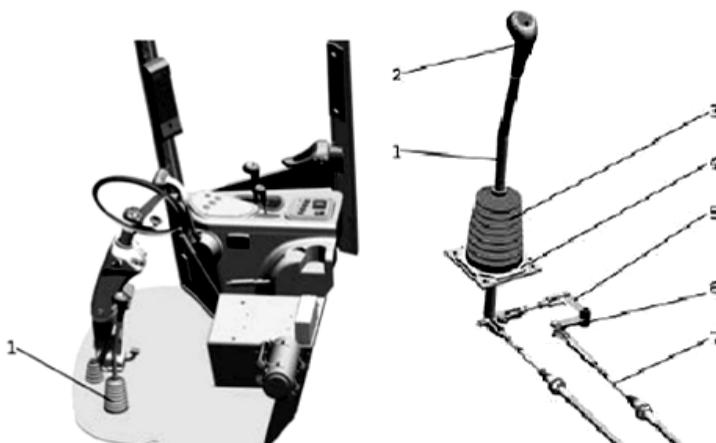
Управление редуктором режима реки: 1 – рычаг управления редуктором режима реки; 2 – рукоятка; 3 – чехол; 4 – опора; 5 – блок рычагов; 6 – вилка; 7 – трос дистанционного управления
